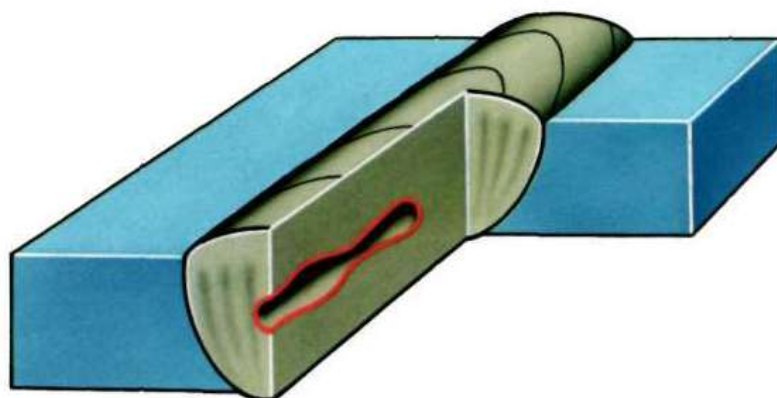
Дефекты сварного шва по типу продолговатой газовой полости
